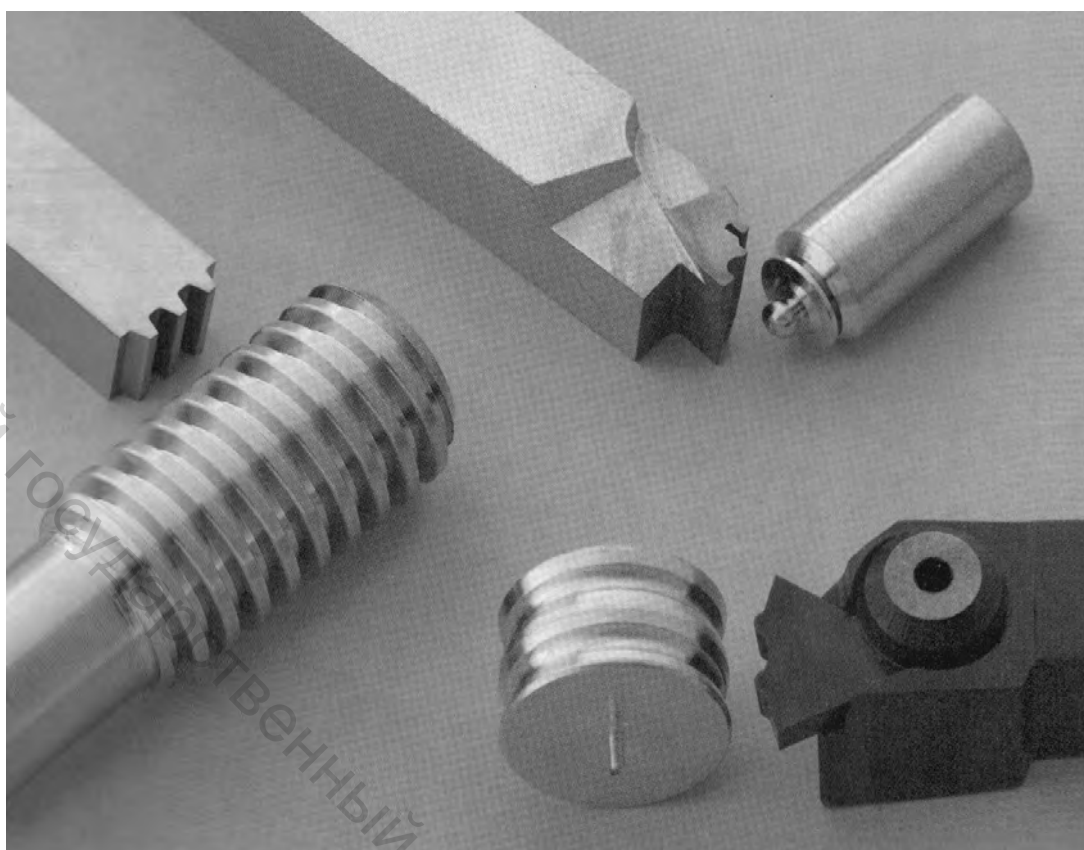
Примеры вырезной обработки режущих кромок токарных резцов
